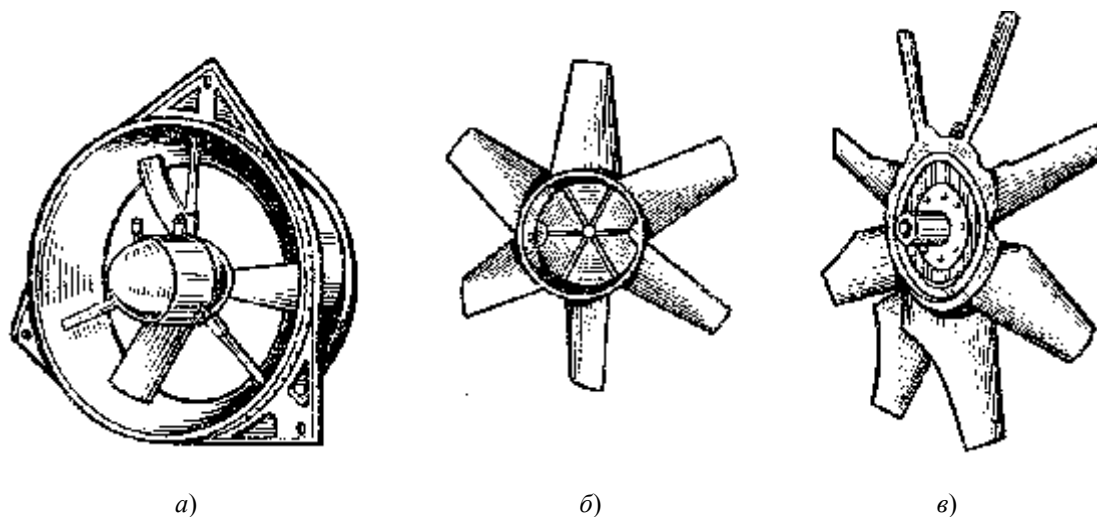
Осевой вентилятор: *а* – общий вид; *б* – сварное лопаточное рабочее колесо;
